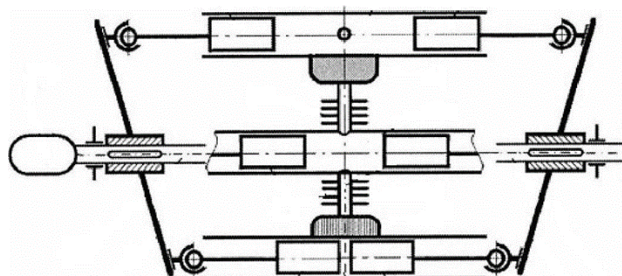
Схема осевого двигателя без отдачи с PDP с поворотной шайбой и полусферическим подруливающим устройством.
